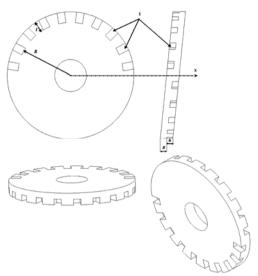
Конструкция самоосциллирующего круга с прерывистой режущей поверхностью.
